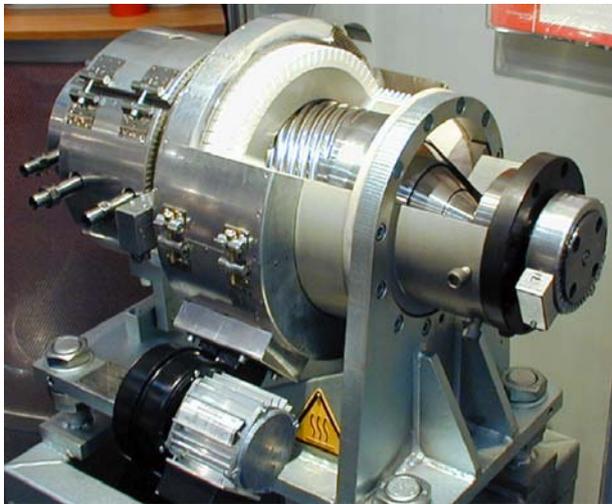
5-Schicht Rohrcoextrusionswerkzeug mit Heiz-Kühleinheit aus Keramikrippensteinen
